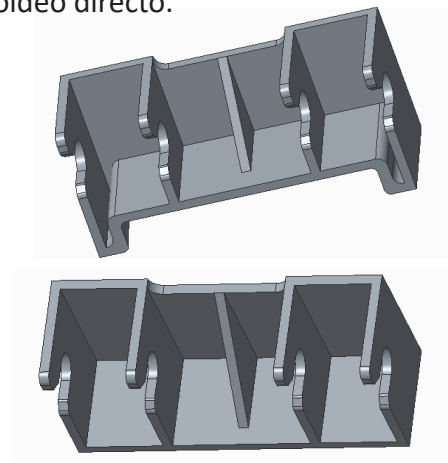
Vistas generales de las dos opciones de pieza clipada: arriba, realzado completo; abajo, realzado simple.
